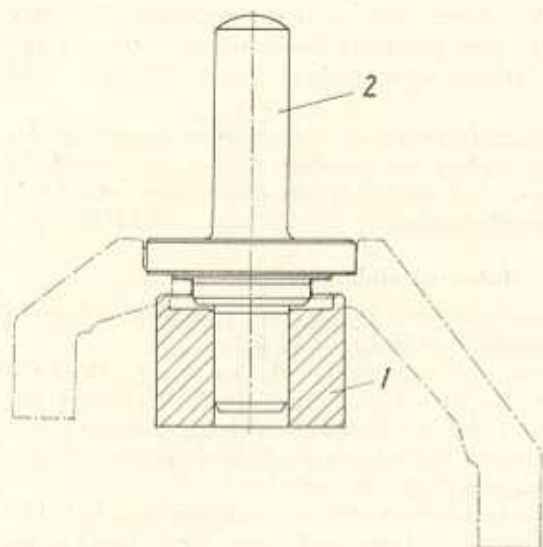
Einpressvorrichtung für den Wellen-Dichtring in das Schwenklager (W-210 747)
